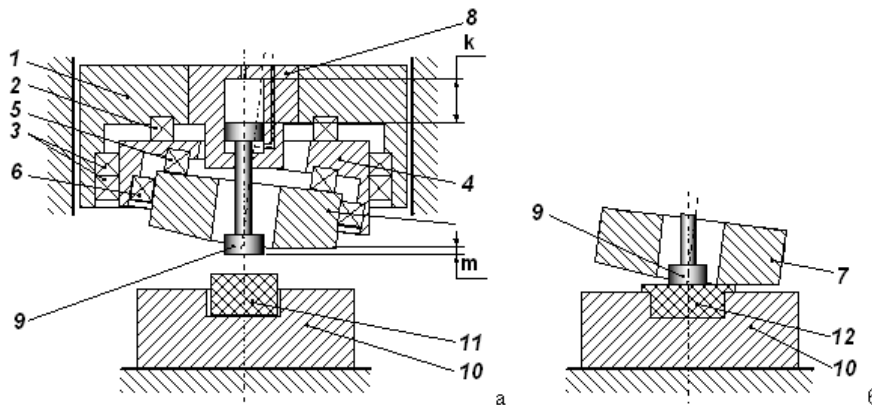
Конструкция механизма обкатывания с устройством для центральной фиксации заготовки: а – начальная стадия обработки; б – конечная
